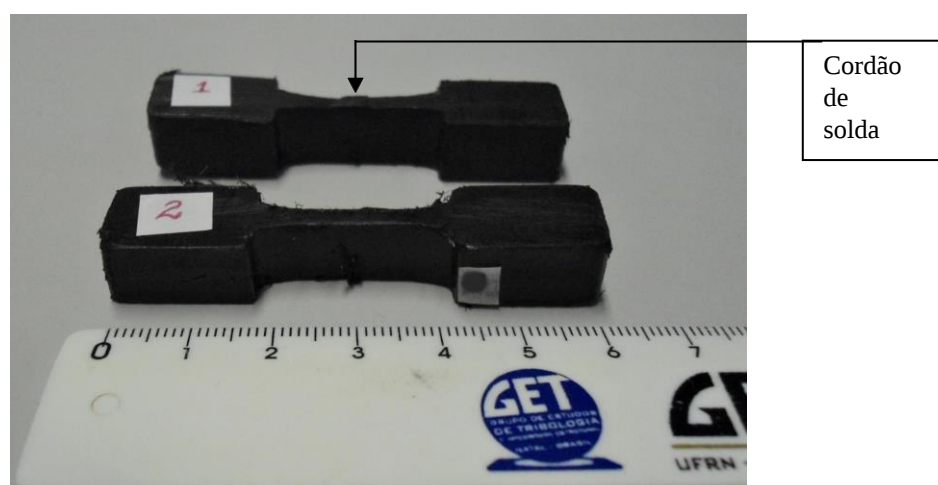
Corpos de prova em PEAD (1) com cordão de solda, (2) Sem cordão de solda.
